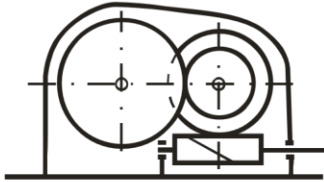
Двоступеневий горизонтальний редуктор з циліндричними колесами
